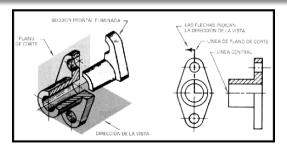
Plano de corte corrido (Izg.) y dibujo detallado con dos vistas en corte (Der.).
